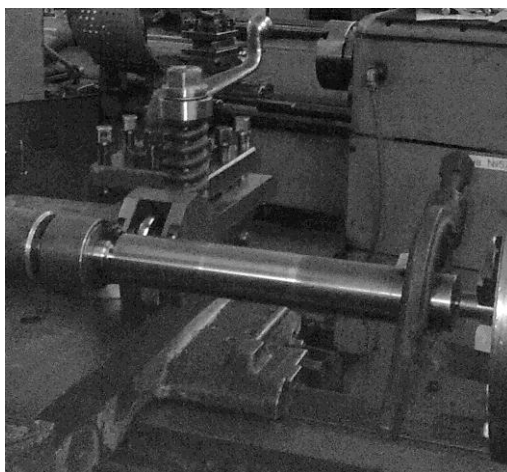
Обкатывание вала роликом на токарно-винторезном станке 1К62
